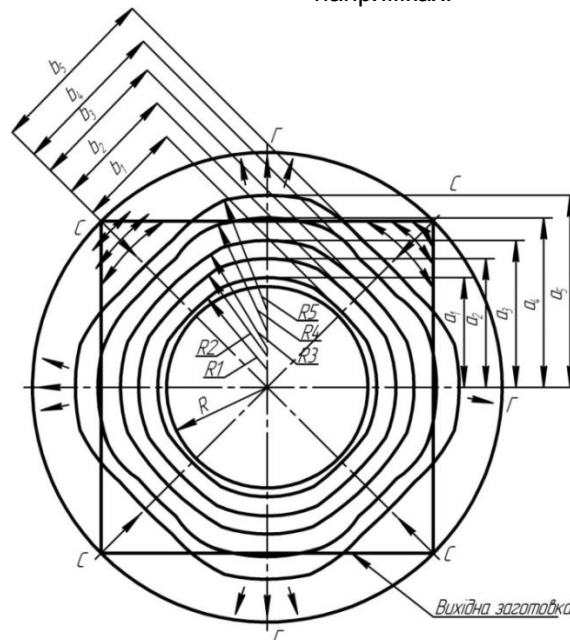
Схема переміщення металу штампуванням обкочуванням з квадратної заготовки в фланцевій частині деталі: Г - Г - лінія переважання радіального переміщення металу; С - С - лінія переважання тангенціального переміщення металу.
